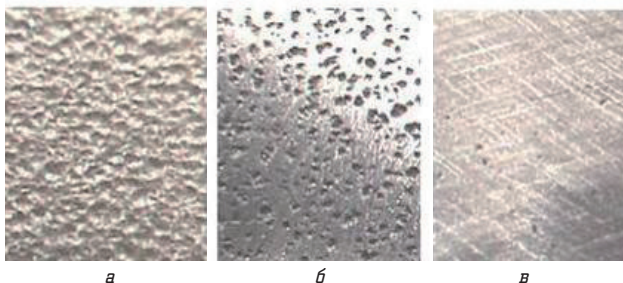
Поверхні алюмінієвого сплаву Д16Т після обробки: а — дробом; б — чорнкової зачистки; в — фінішної зачистки [8]
